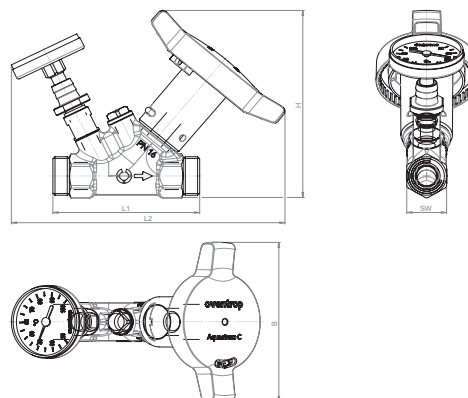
Abmessungen Seitenansicht / Frontansicht Außengewinde
